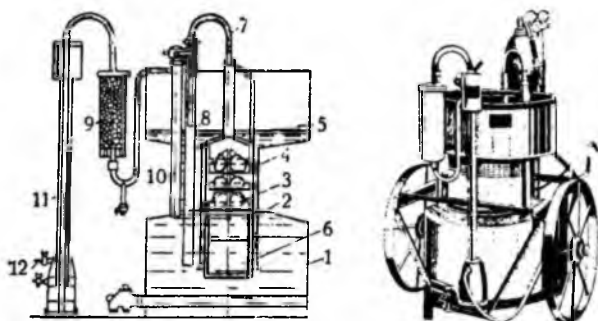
Общий вид и схема ацетиленового генератора СВ:
